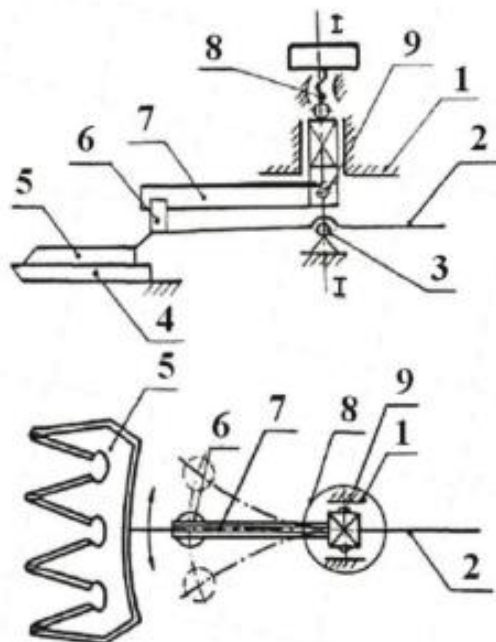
Кінематична схема машинки з пружним елементом: 1 - корпус; 2 - важіль; 3 - центр обертання; 4 - гребінка; 5 - ніж; 6 - шарнір; 7 - упор; 8 - гвинт; 9 - заклепка
